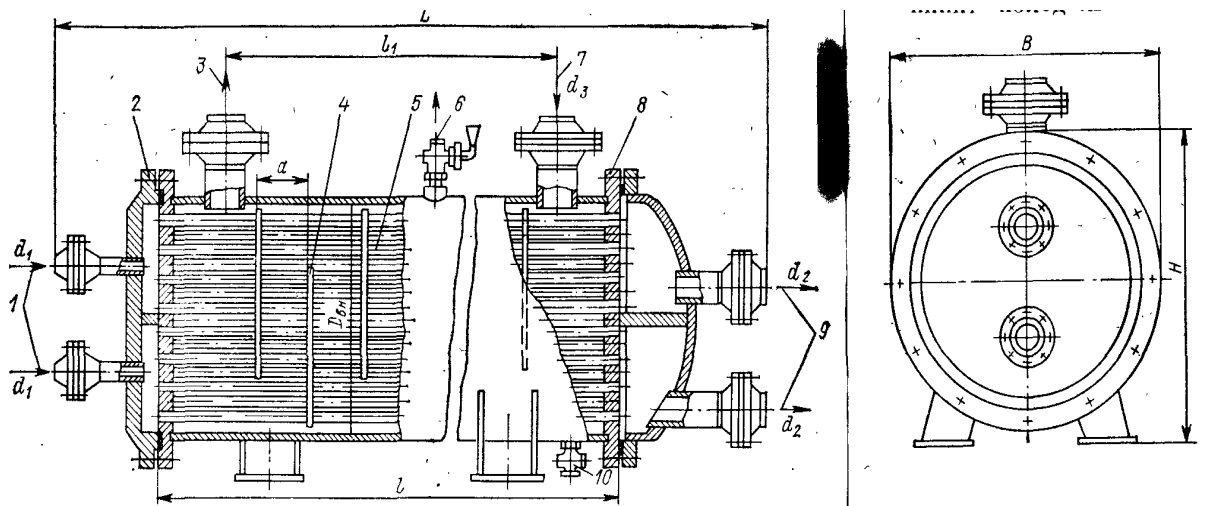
Кожухотрубний випарник з кипінням робочої речовини всередині прямих труб: 1,9- вхід і вихід робочої речовини; 2- кришка; 3,7- вихід і вхід розсолу; 4- перегородки; 5- кипятильні труби; 6- вентиль для продувки; 8- трубна решітка; 10- злив розсолу
